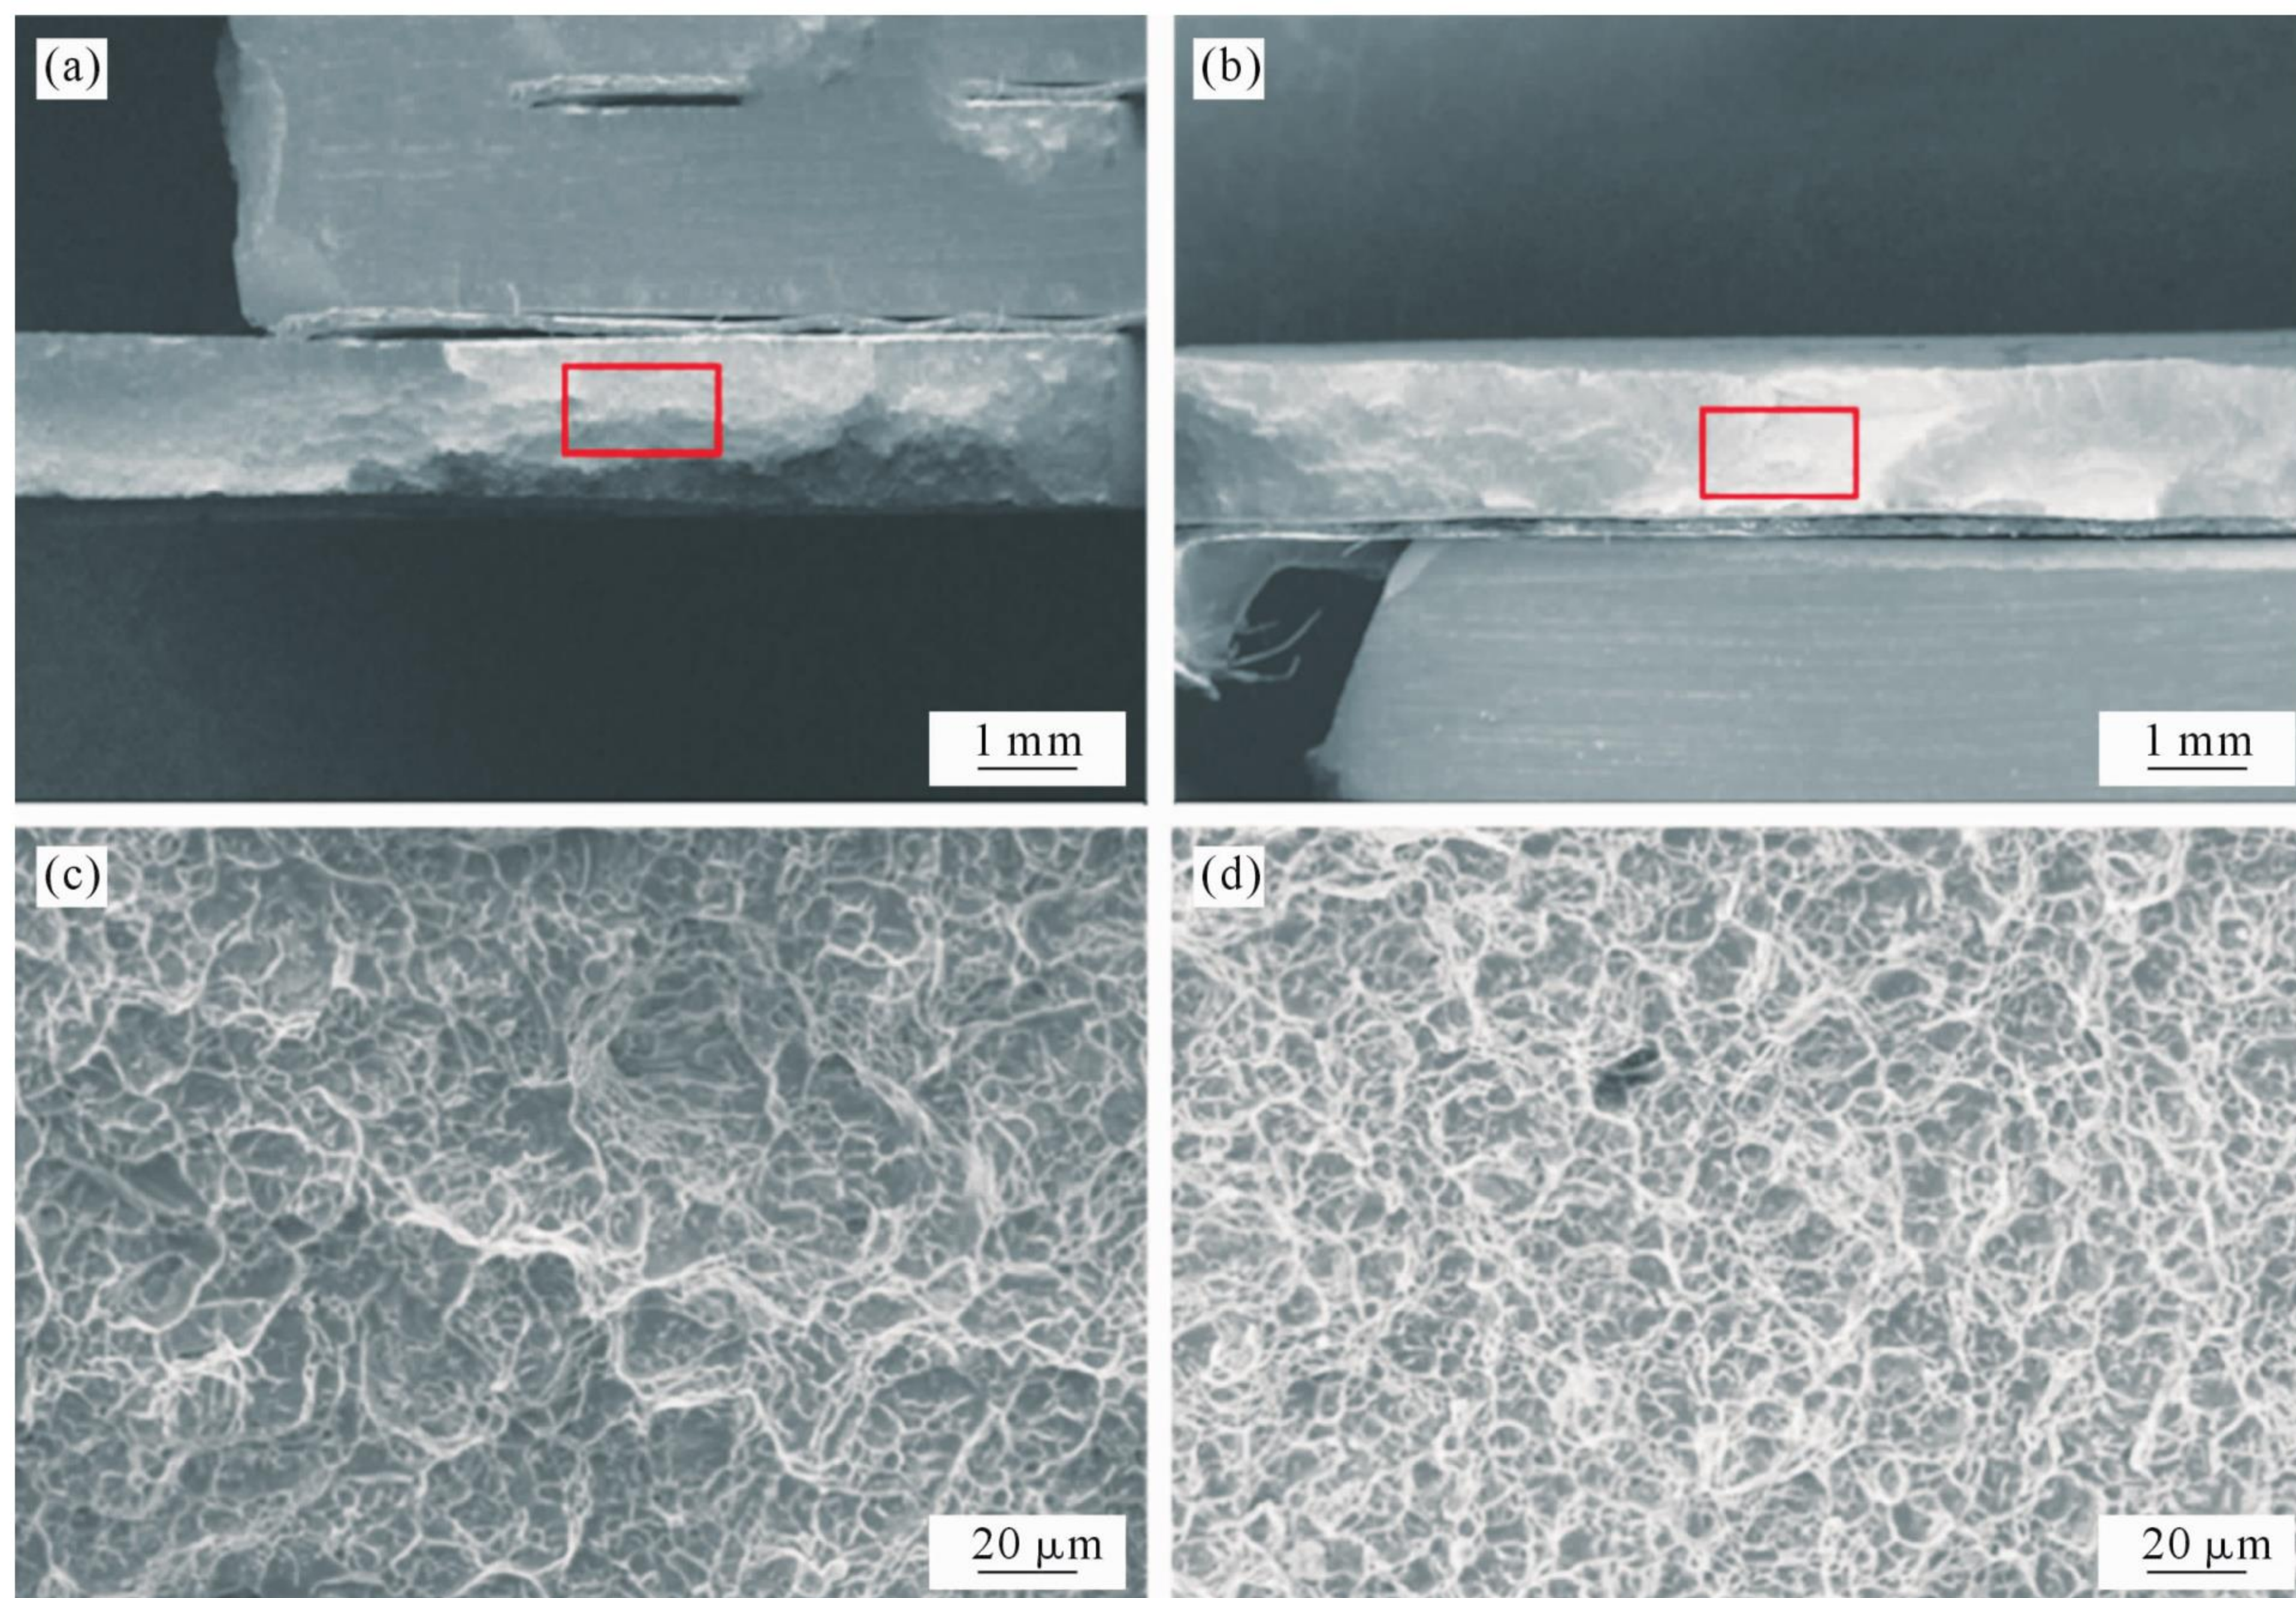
TA15 焊接接头断裂试样断口形貌:(a) 室温拉伸断口宏观形貌;(b) 225 °C 拉伸断口宏观形貌;(c) 室温拉伸断口微观形貌,图(a)矩形框的放大图;(d) 225 °C 拉伸断口微观形貌,图(b)矩形框的放大图
